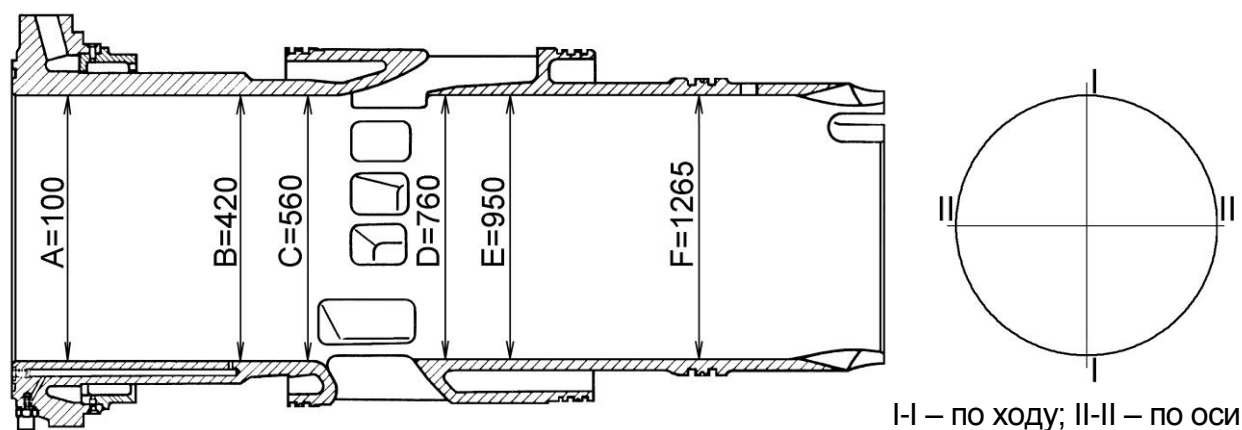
Схема обмеров втулки цилиндра дизеля типа 8ZD72/48
